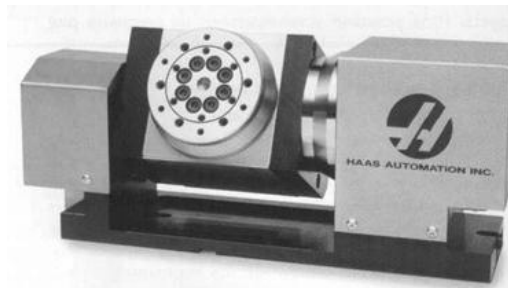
ТК110 - двовісний похило-поворотний стіл
